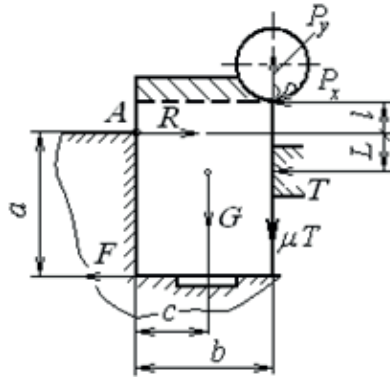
Схема сил, які діють на затиснуту заготовку при фрезеруванні
